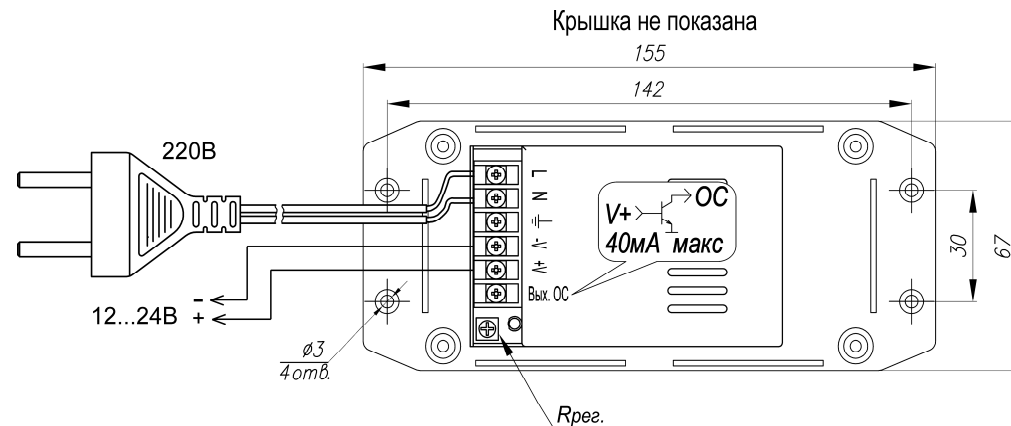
Устройство, габаритные и установочные размеры, подключение БП-18Вт
